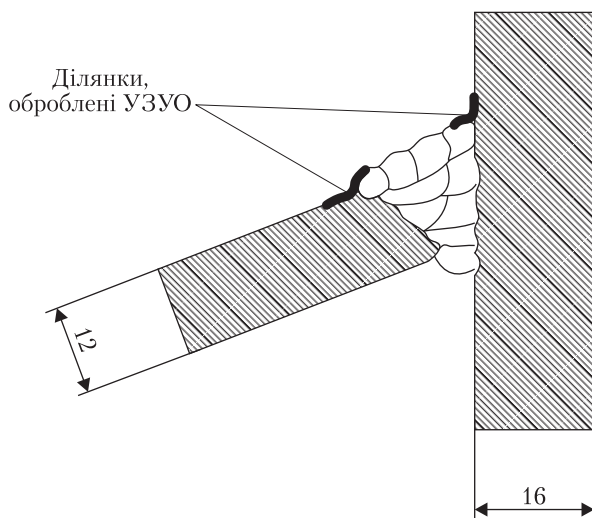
Місця обробки зварного шва за допомогою УЗУО
